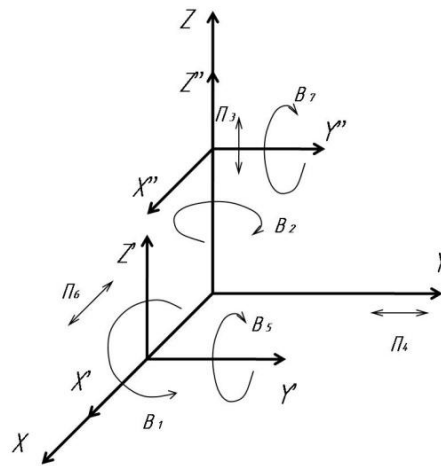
Относительная ориентация движений исполнительных органов универсального фрезерного станка
